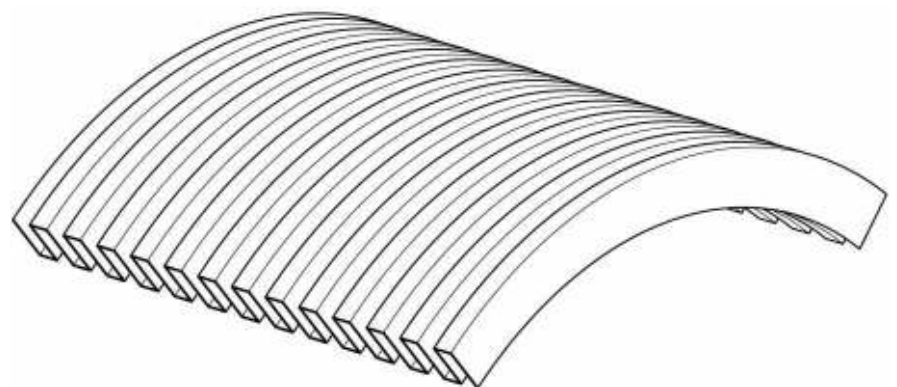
auch entlang der Stege sind mit geeigneten Biegemaschinen Verformungen möglich
